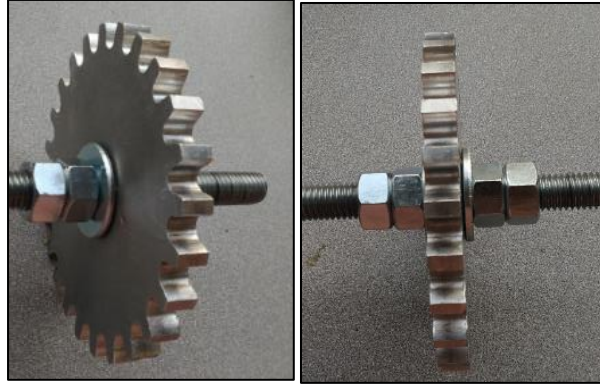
engranajes contruidos mediante CNC (fuente: fotografía propia).
